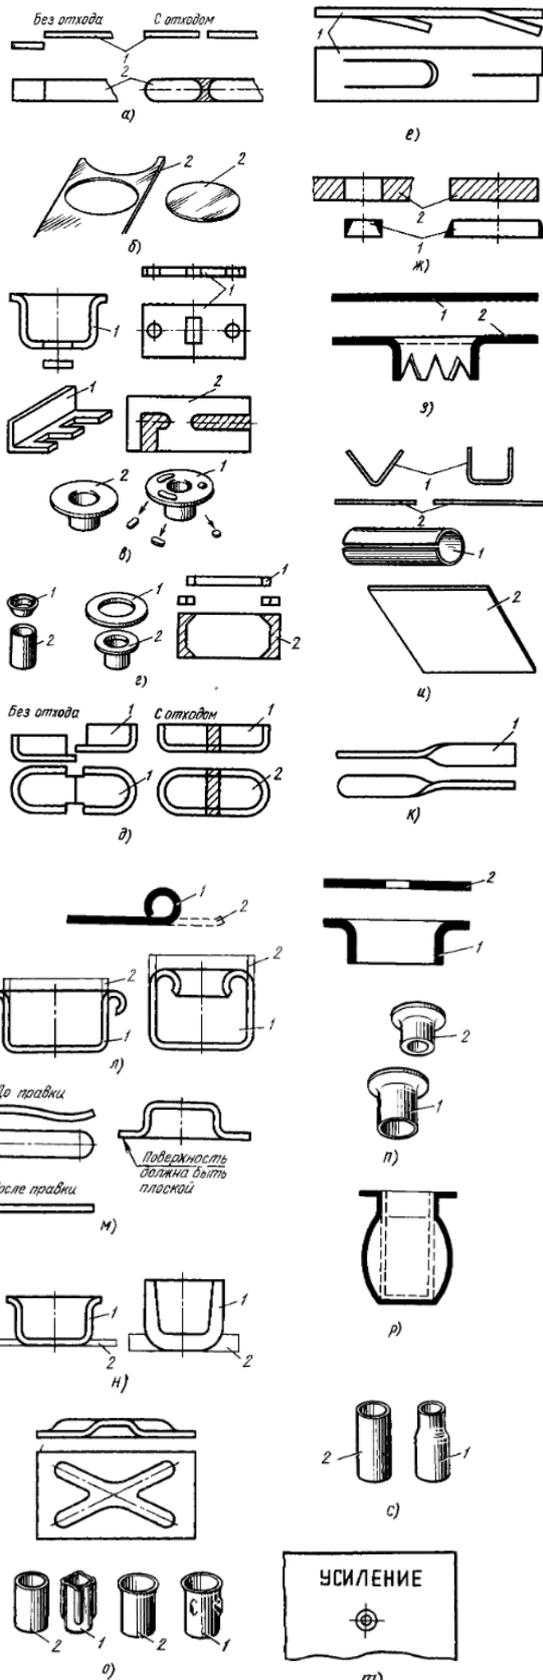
Детали (1) и исходная заготовка (2), полученная операцией листовой штамповки:
